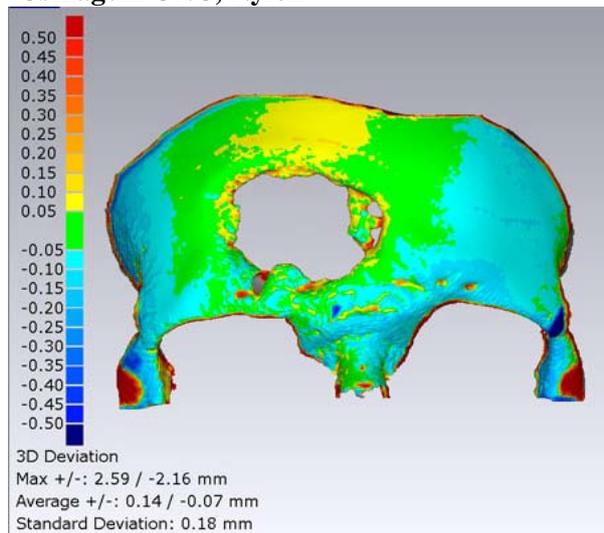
Precisão do protótipo fabricado por usinagem CNC de Nylon.
